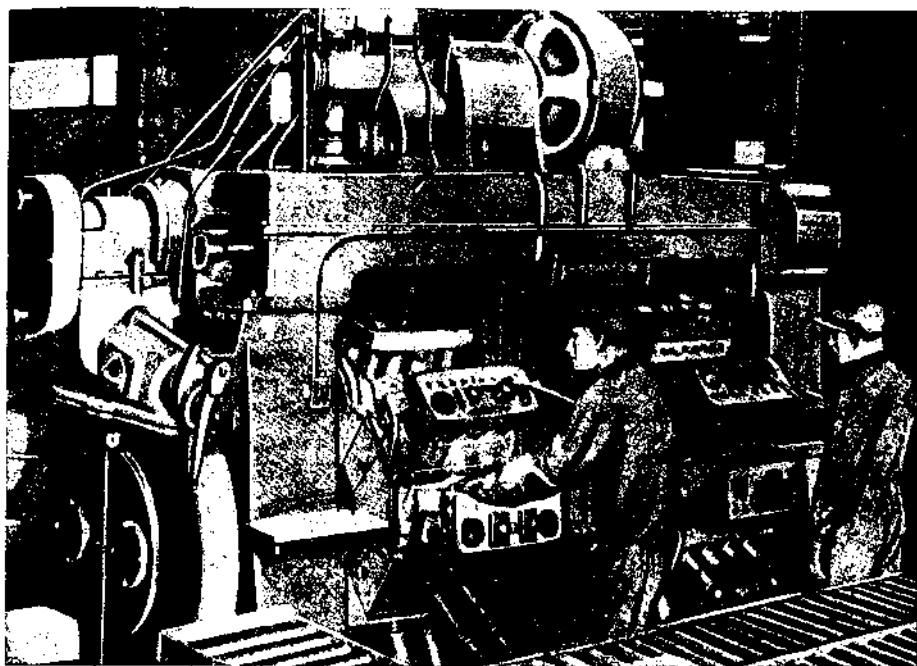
Вторая фрезерная операция на блоках у Форда.
